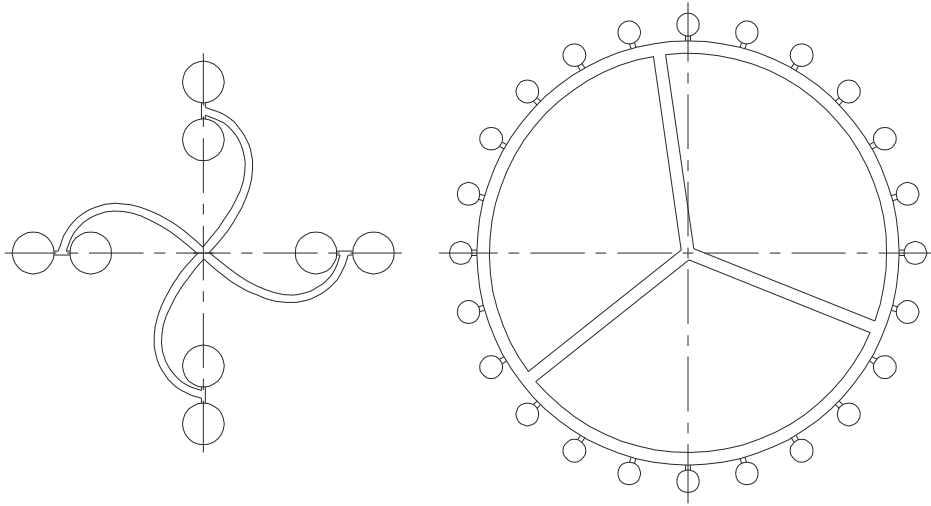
Dişi Kalıp(solda) ve Erkek Kalıp(sağda)
